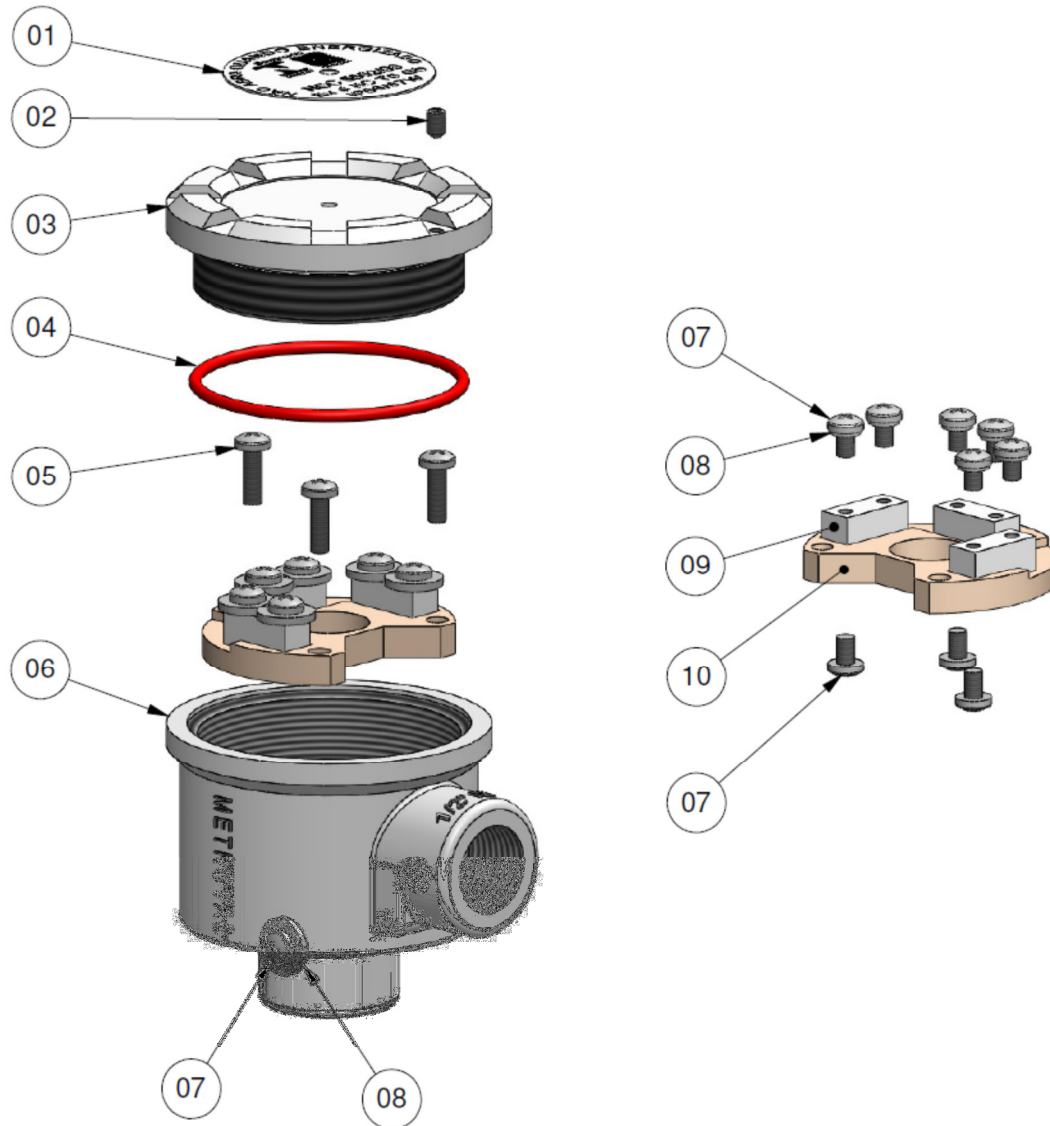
Desenho explodido da Caixa de Passagem CF8M
